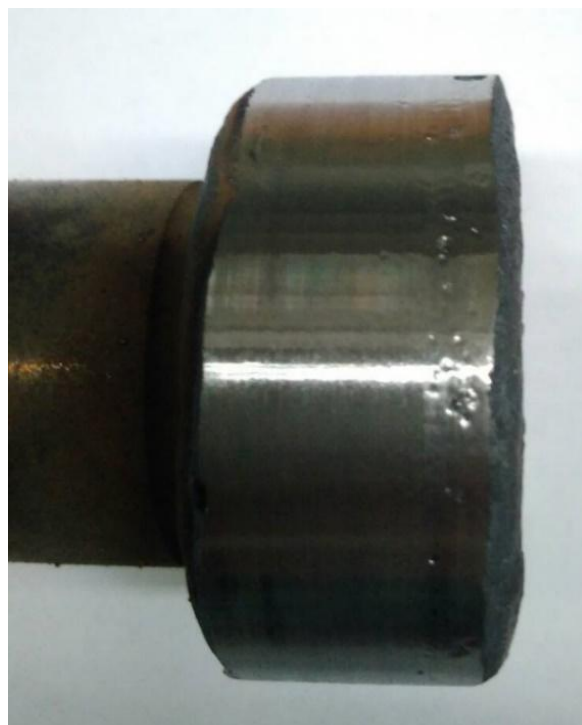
Зразок після проточки поверхні що наплавлялась
